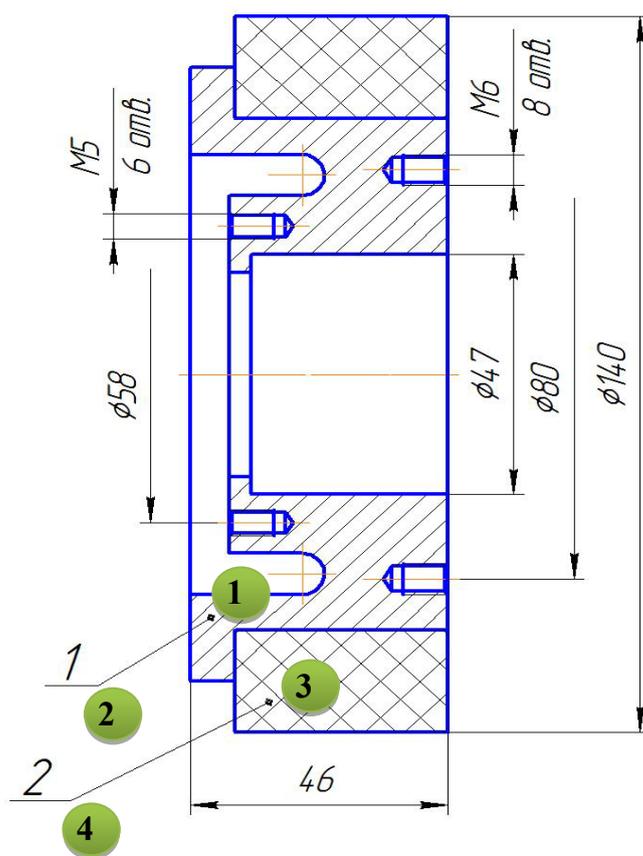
Порядок простановки позиций на сборочном чертеже
